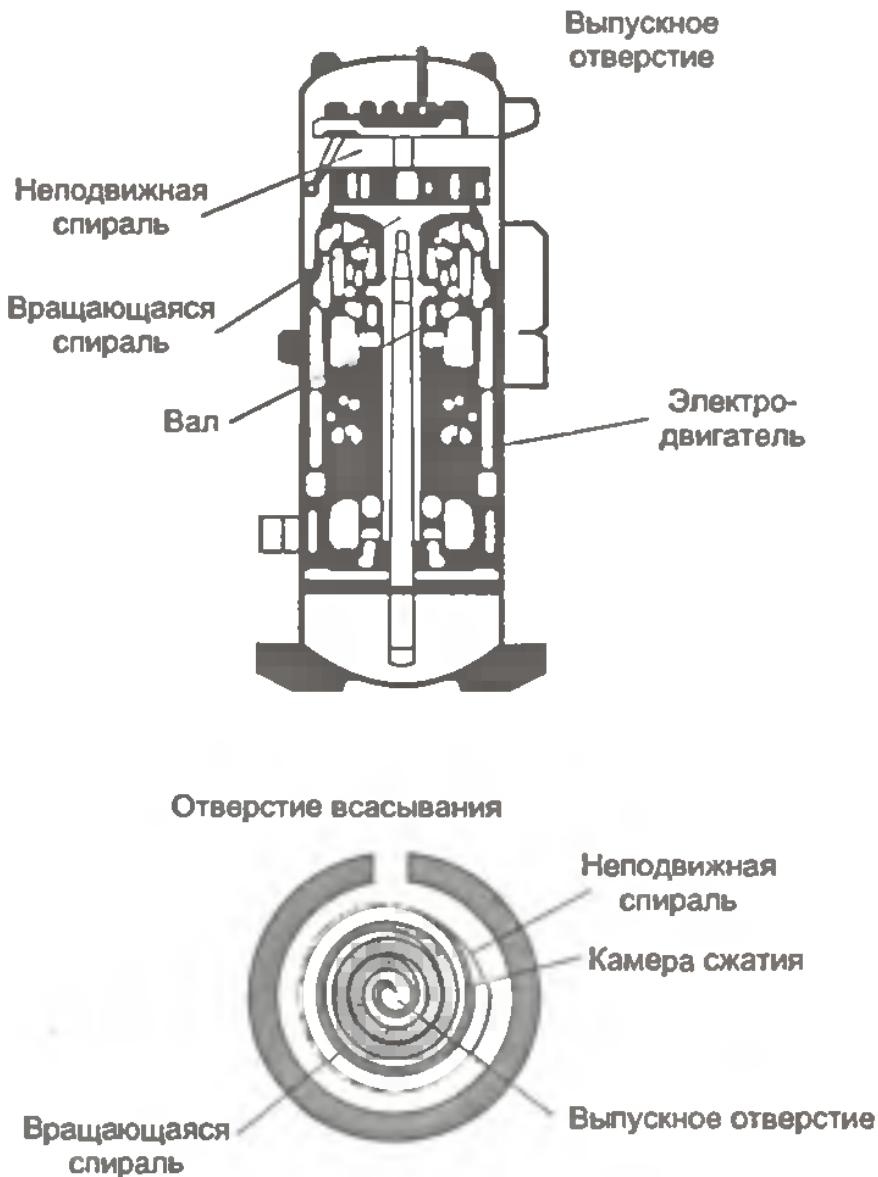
Спиральный компрессор (компрессор Scroll)
